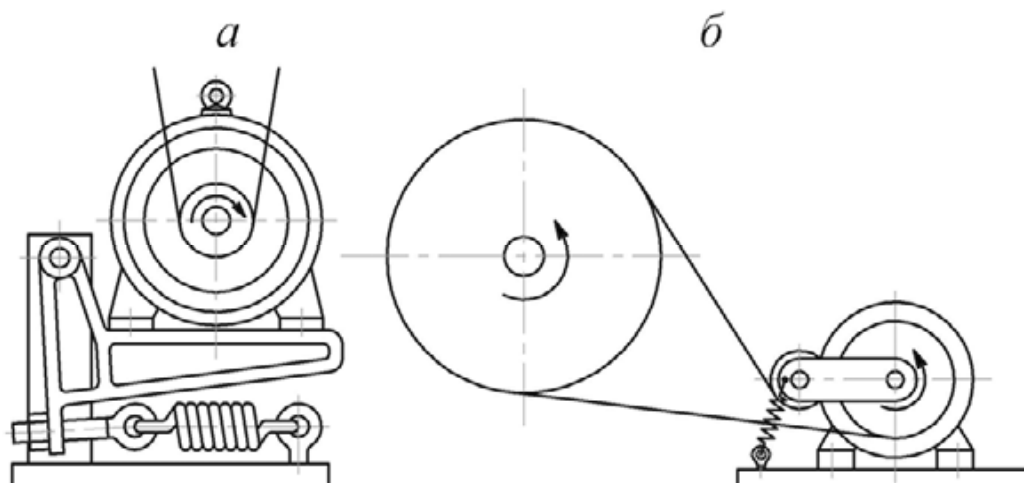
Способы автоматического натяжения ремня с использованием массы качающегося двигателя и пружины
